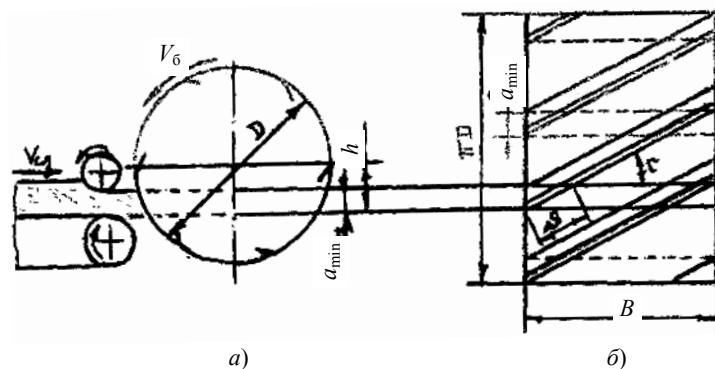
Схема режущего аппарата барабанного типа (а) и развертка ножевого барабана (б)
